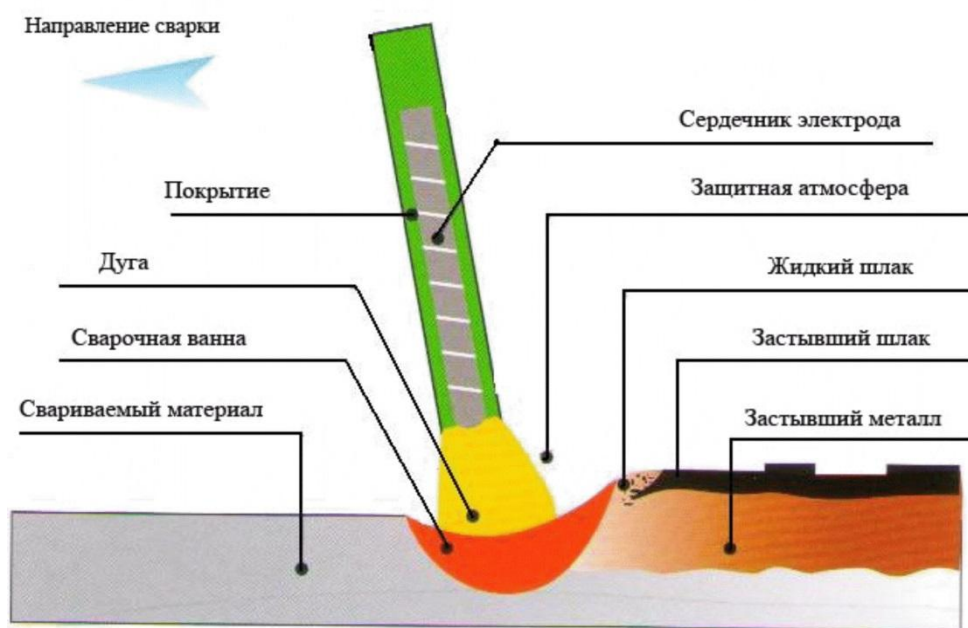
Схема ручной дуговой сварки штучными электродами
